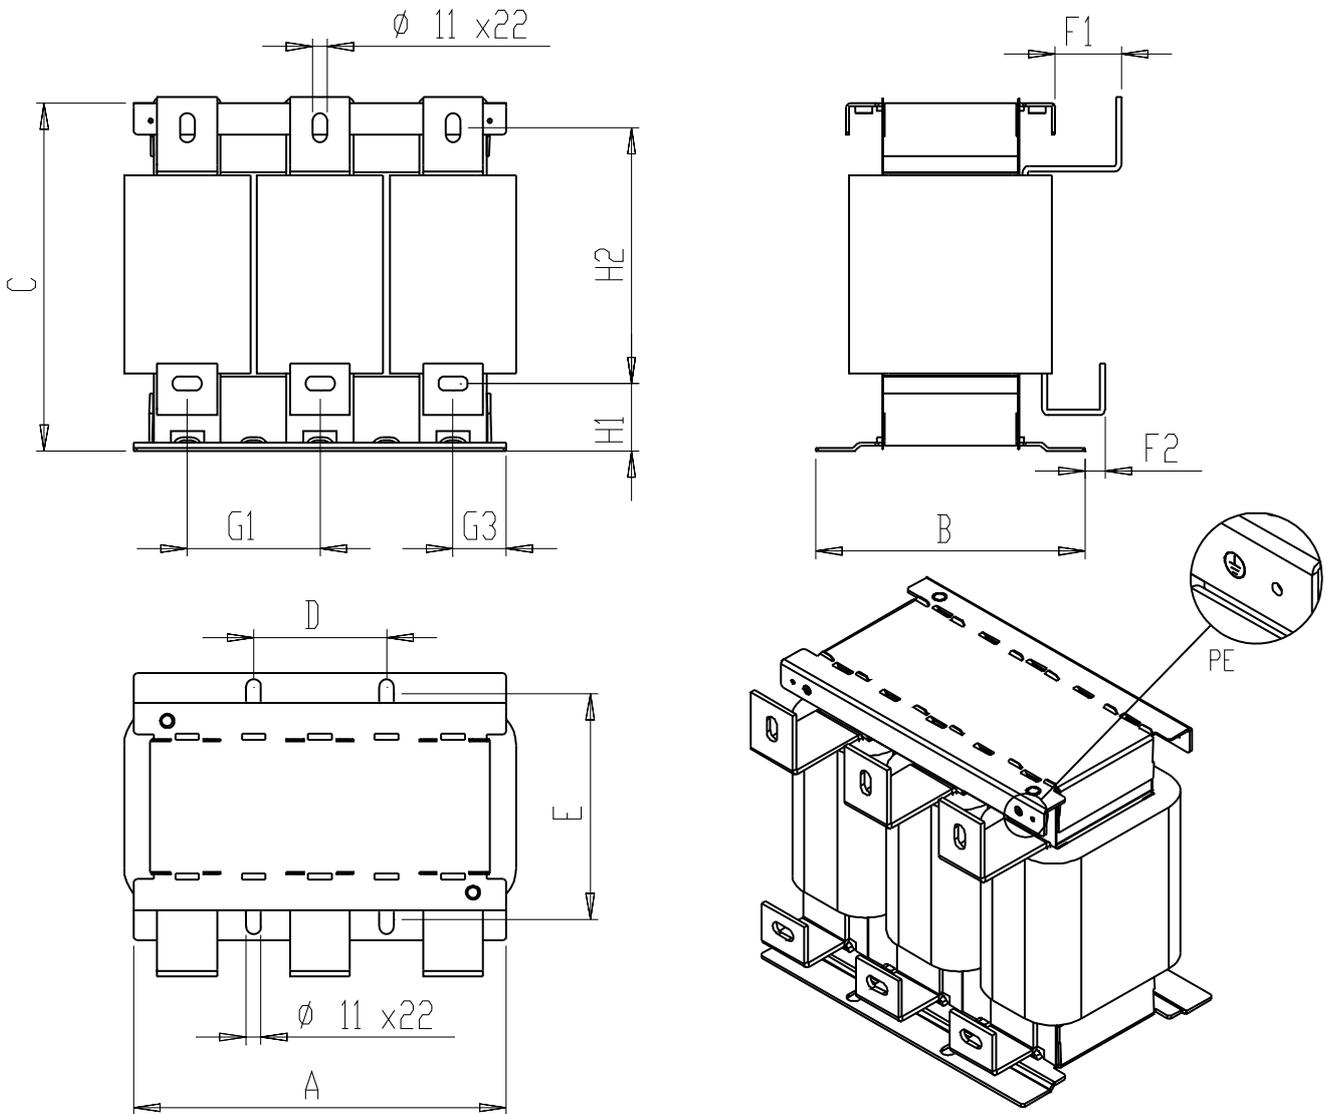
Disegno quotato bobina di rete 6SL3000-0EE36-2AA0
